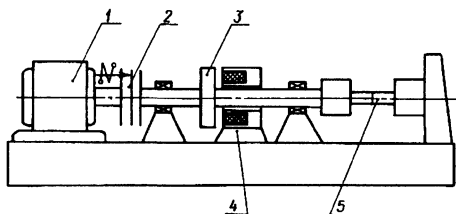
Схема машины для инерционной сварки трением с электромагнитным силовым приводом:
